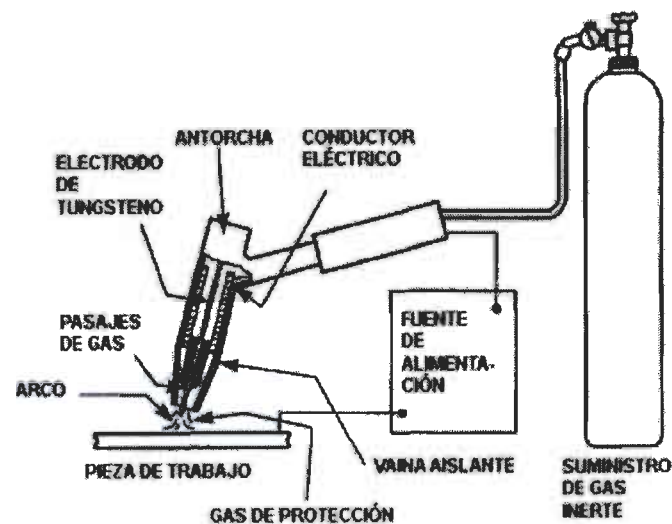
Equipo proceso de soldadura GTAW (15).
